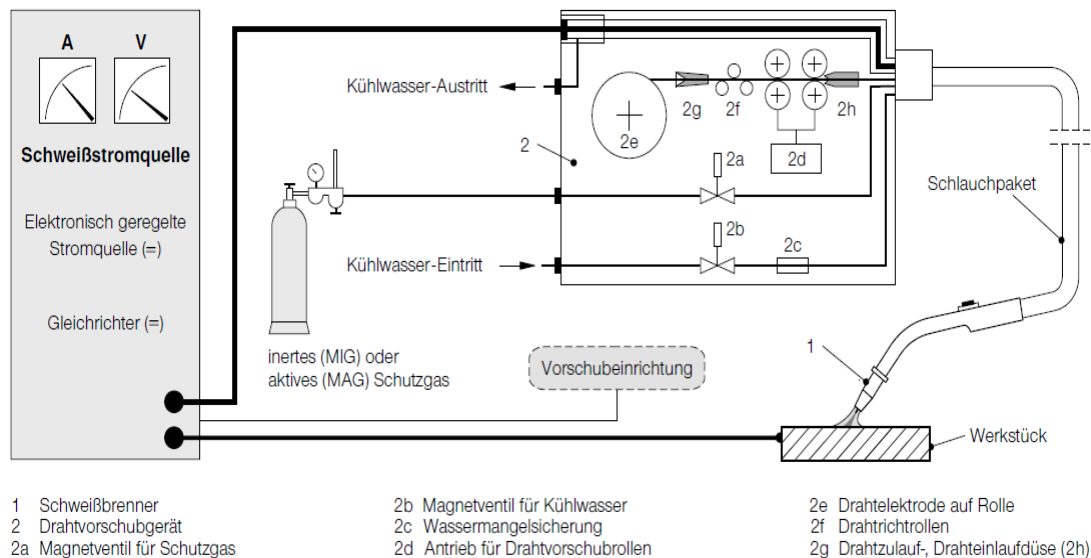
Wassergekühlte MIG-/MAG-Schweißanlage [9]
